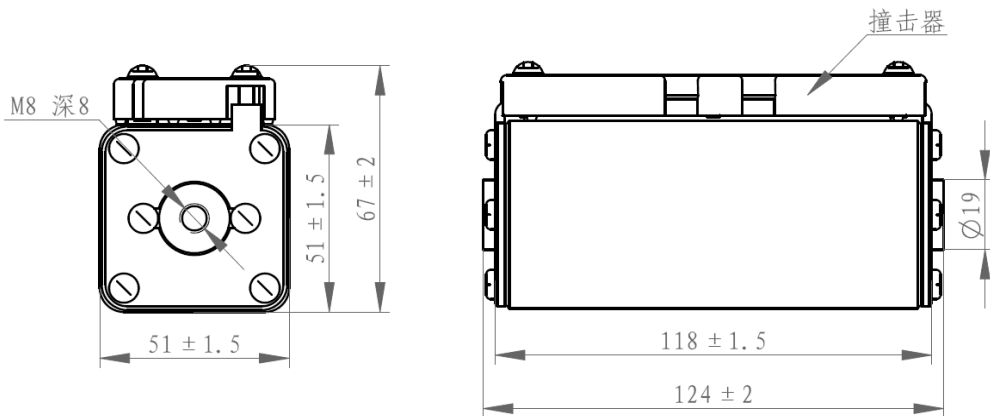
STFG10-1000/400基本型的外形尺寸和安装尺寸
